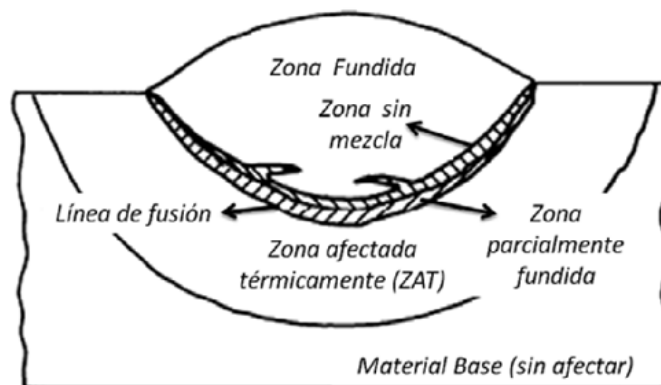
Zonas presentes en un cordón de soldadura.
